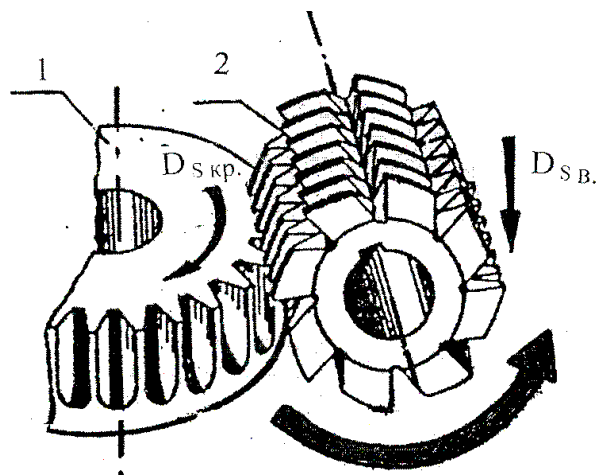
Схема зубофрезерования на зубофрезерном станке:
